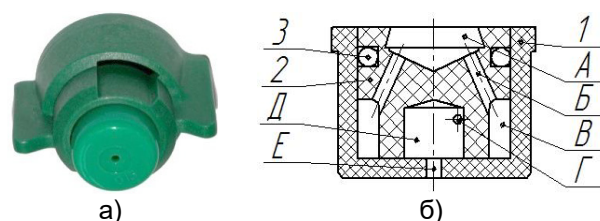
Загальний вигляд (а) і конструктивна схема (б) полімерного відцентрового розпилювача.
